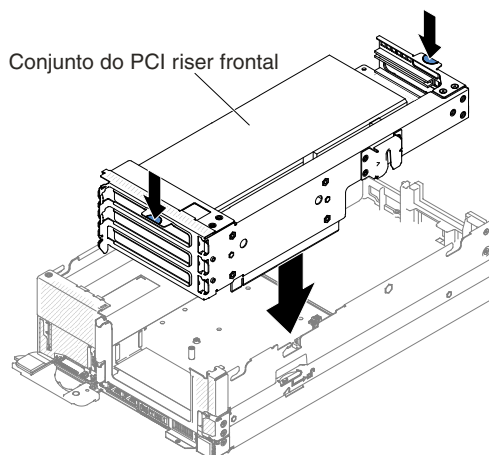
Instalação do conjunto do compartimento da placa riser PCI frontal
